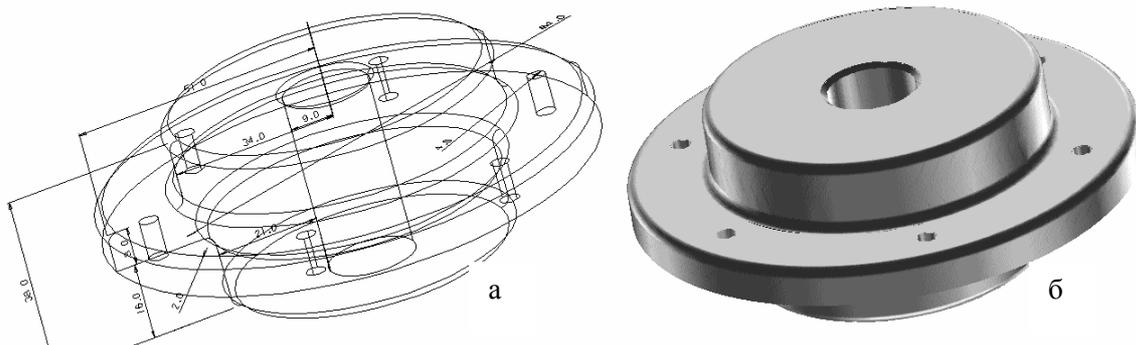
Каркасный вид детали с размерами (а) и ее фотографическое изображение (б) (detail.gif)
